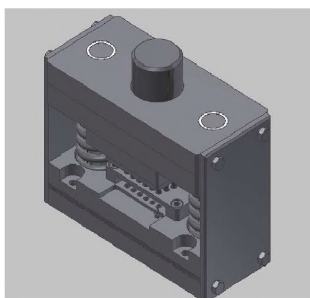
3D-модель приспособления для пробивки отверстий в терке ANKLEPF
